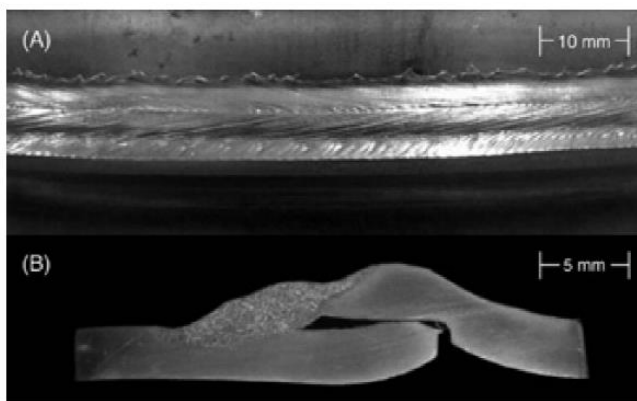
Cordão soldado na selagem de um compressor com processo TIG autógeno à 1,5 m/min. Aspecto superficial em (A) e secção transversal
